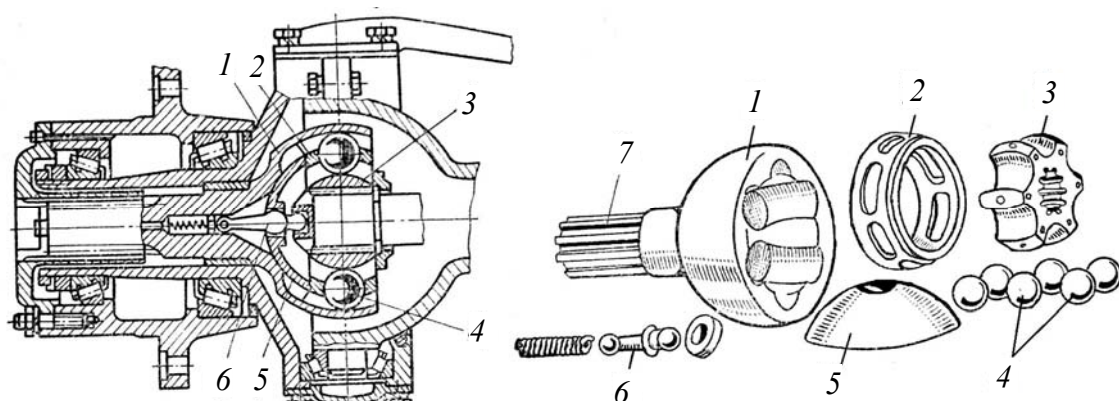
Шариковый карданный шарнир равной угловой скорости с делительным рычажком: 1 – чашка сферическая; 2 – сепаратор; 3 – звездочка ведущая; 4 – шарики; 5 – чашка направляющая; 6 – рычажок делительный; 7 – вал ведомый
